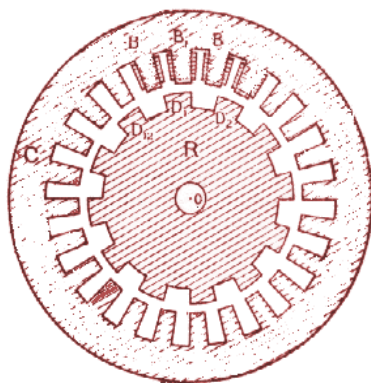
Machine asynchrone à rotor massif rainuré
